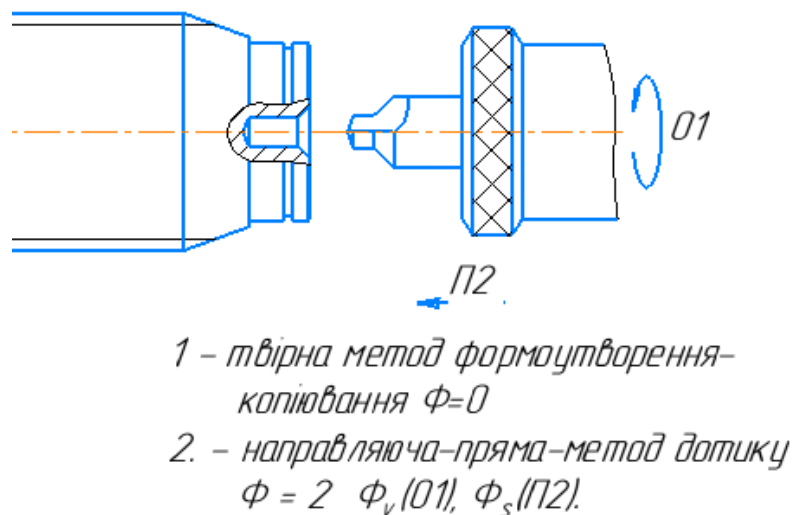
Використання центрального свердла (формоутворюючі рухи)
